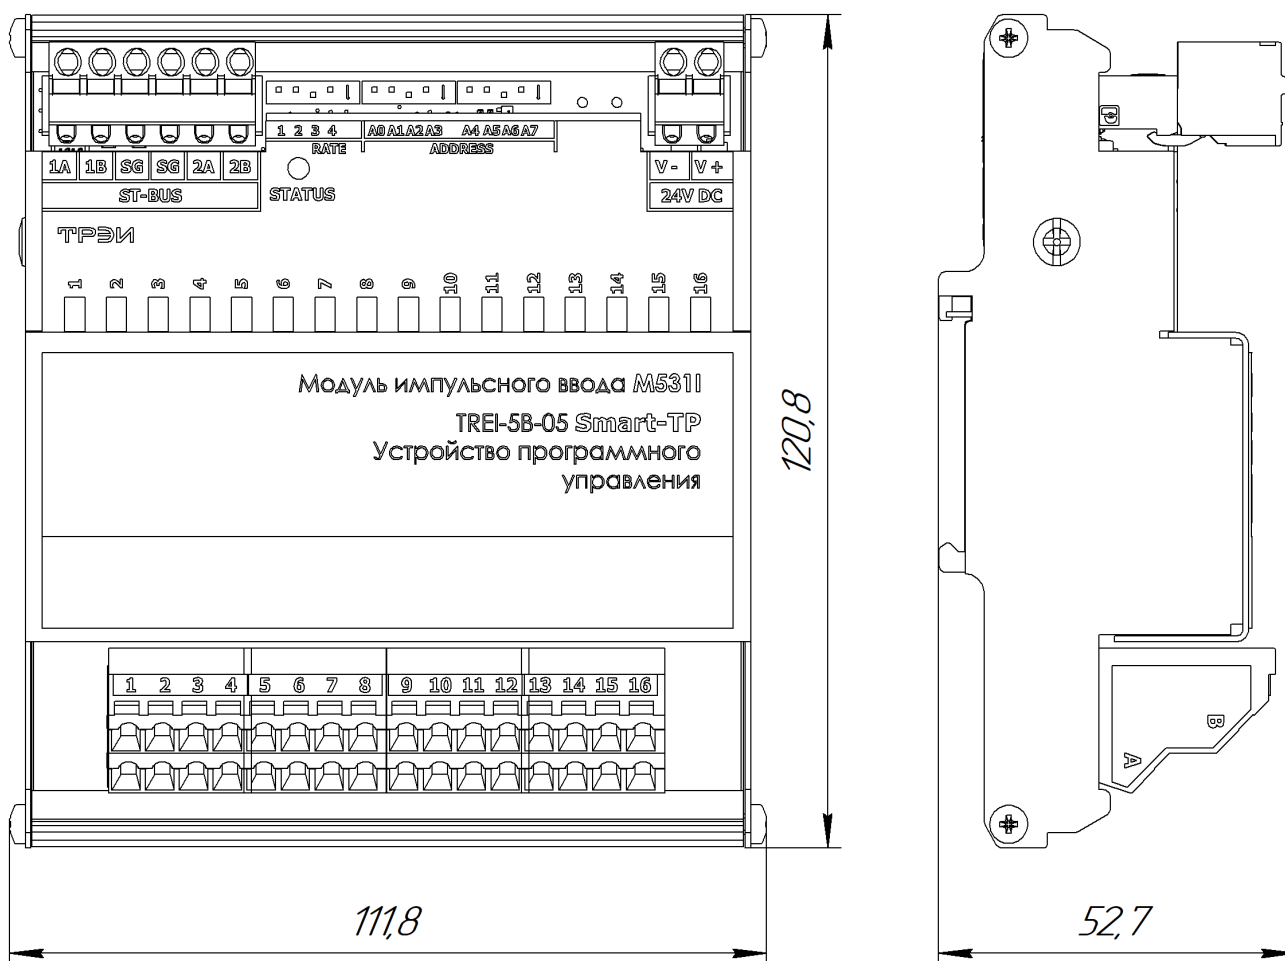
Чертеж общего вида M5311 с указанием габаритных и присоединительных размеров
